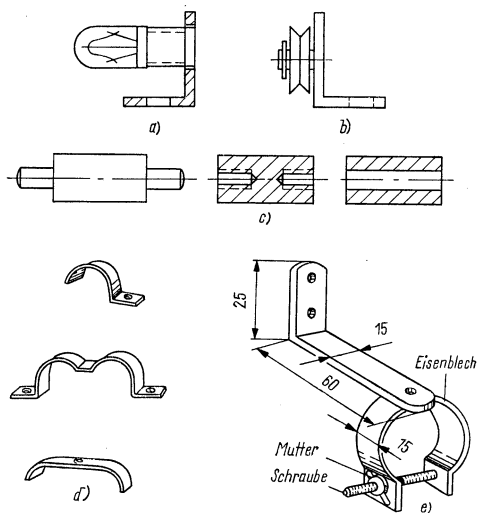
Befestigungsteile; a — Winkel für Skalenlampe, b — Winkel für Seilrolle, c — Abstandsstücke, d — Befestigungsschellen für Elektrolytkondensatoren usw., e — Halterung für ein magisches Auge (z. B. 6 E 5)
